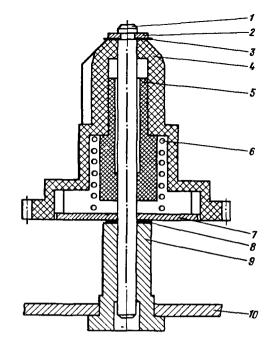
Шпиндель подающего узла: 1 — ось; 2 — фиксирующая шайба; 3 — фторопластовая шайба; 4 — шпиндель подающего узла; 5 — втулка подшипника скольження; 6 — пружина; 7 — шайба; 8 — фторопластовая шайба; 9 — втулка с запрессованной осью 1; 10 — шасси
